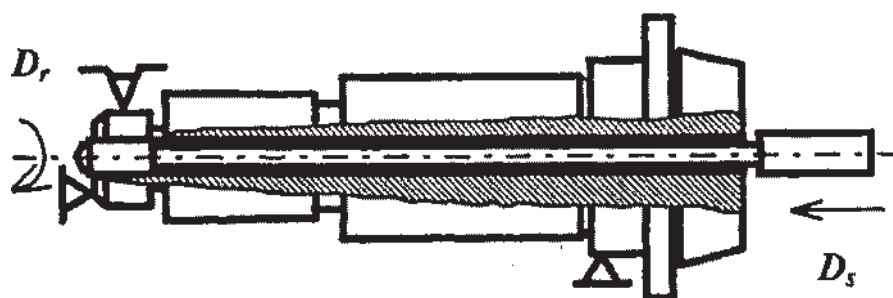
Схема обработки центрального отверстия на горизонтально-сверлильном станке для глубокого сверления
